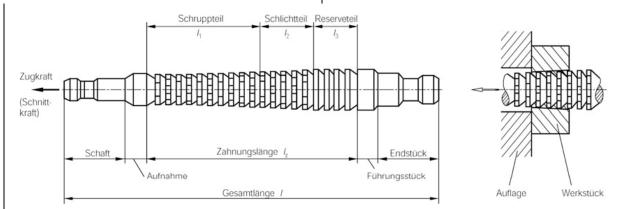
Aufbau eines Innenräumwerkzeugs / Construcția unei broșe pentru prelucrări interioare [GYE 91]
